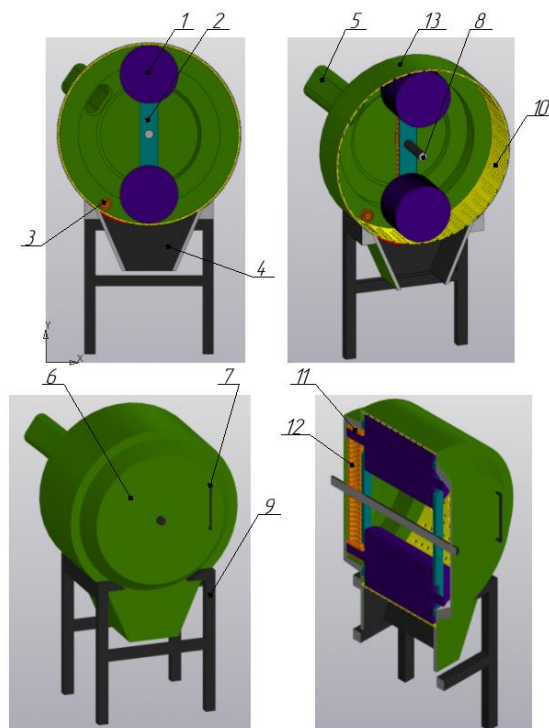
Конструкция пресс-гранулятора с подводом пара и устройством регулирования силы прижатия ролика к материалу: 1-ролик; 2-направляющая роликов; 3-форсунка для ввода пара; 4-разгрузочный патрубок; 5-загрузочное устройство; 6 – дверца; 7-ручка; 8-вал; 9-стойка; 10 – перфорированный барабан; 11-прижимная площадка; 12-пружина
